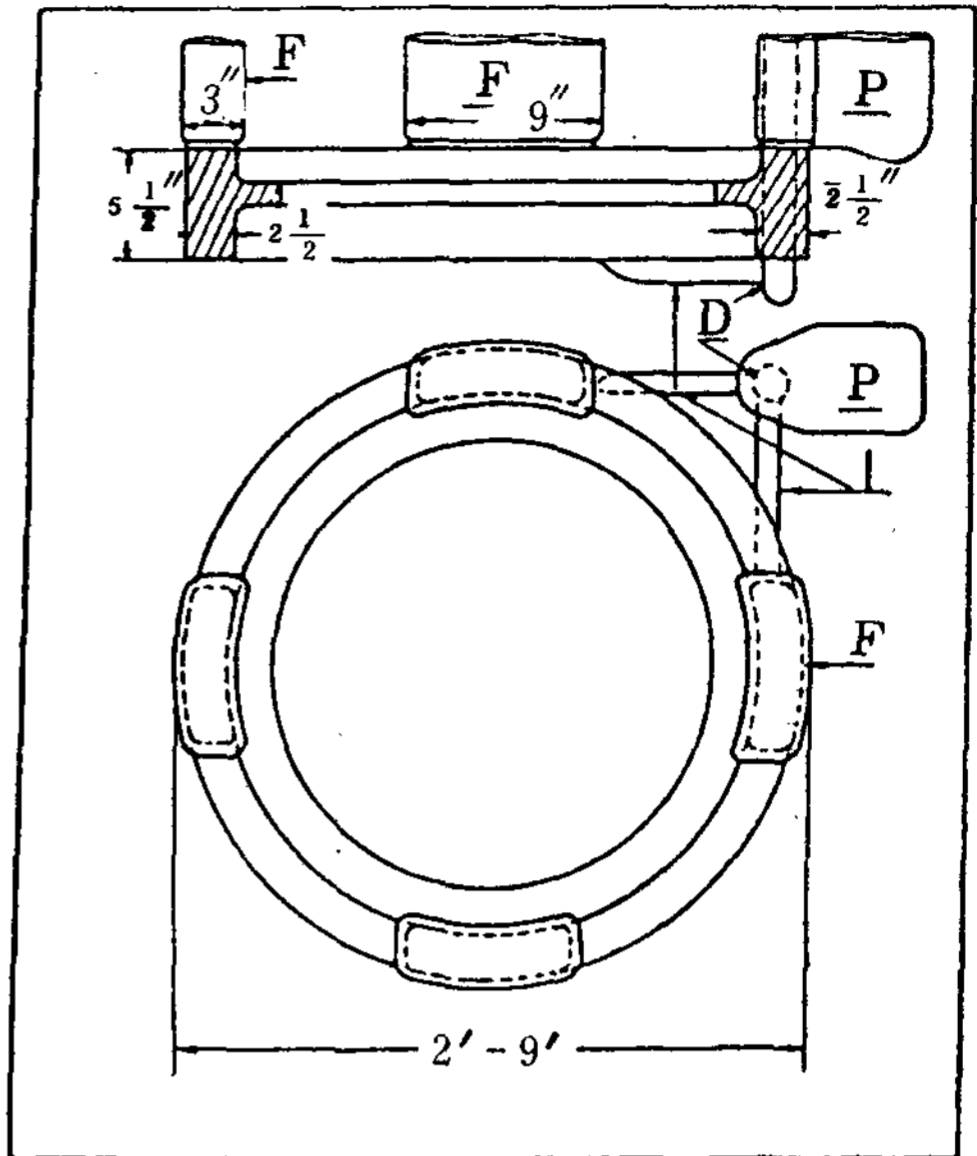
densener를 쓰지 않은 gear-rim blank 주조방안
